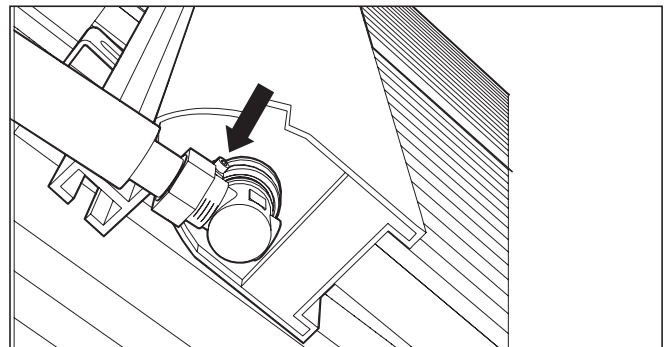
Demontage der hydraulischen Anschlüsse
